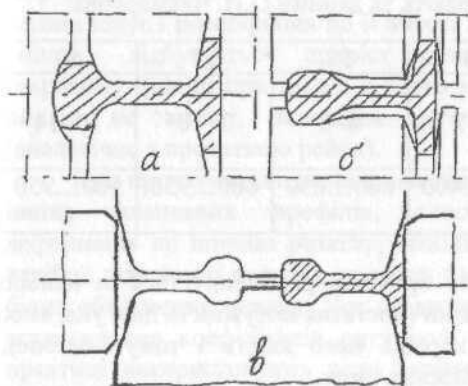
Схема прокатки рейок з використанням багатовалкових калібрів : а-універсальна чотири-валкова кліть; б - допоміжна двошвалкова кліть; в - чистова універсальна кліть з тривалковим калібром.
